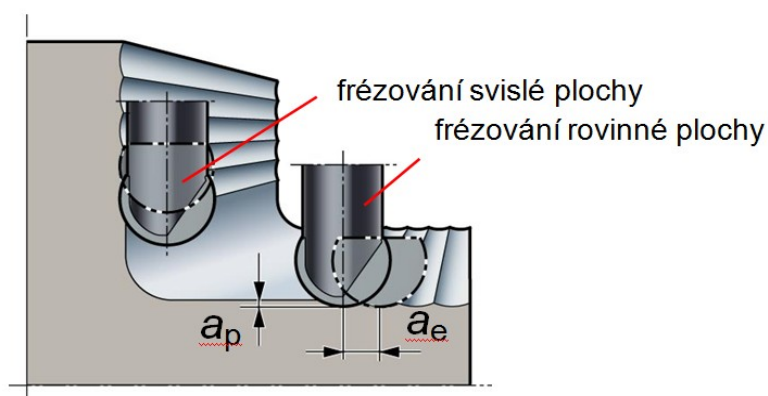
Obrábění tvarové plochy kulovou frézou stopkovou frézou s rádiusem v rohu
